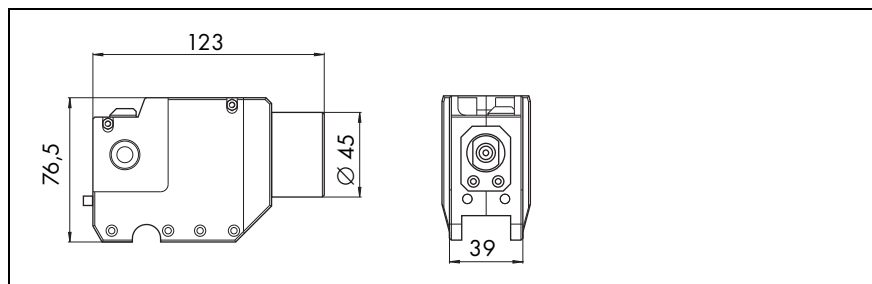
Chaqueta aislante con cuerpo intercambiable
